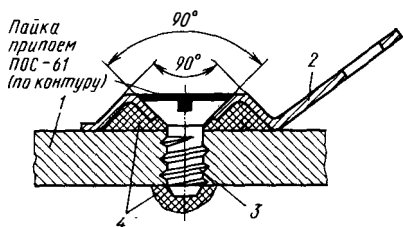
Присоединение лепестка к литому корпусу с помощью самонарезающего винта:
